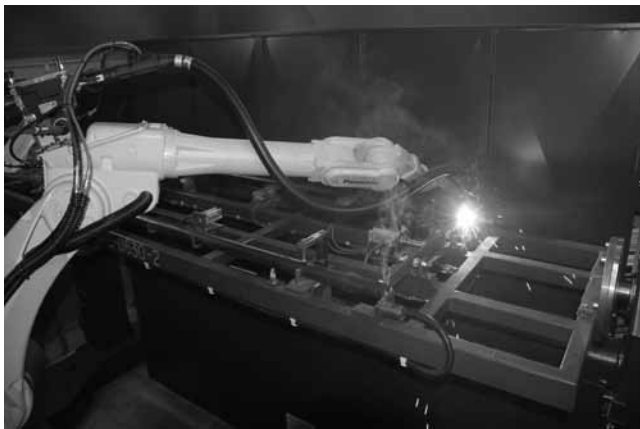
Wirtualny i rzeczywisty system do spawania metodą TIG z uchwytem *Rotating TIG filler
